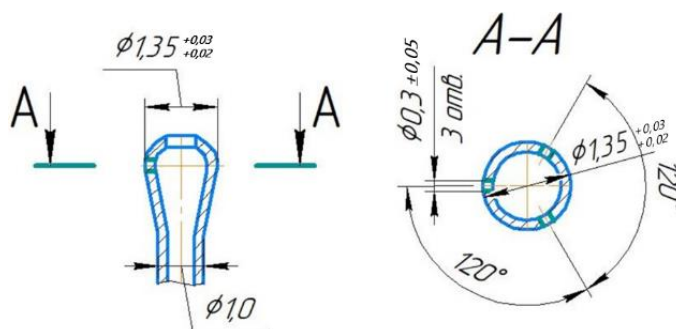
Чертеж-схема прошивки микроотверстий
